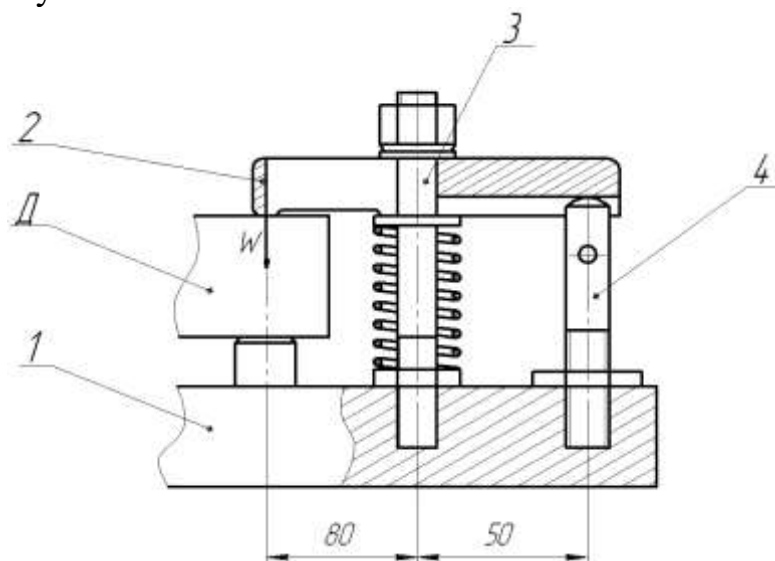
Схема прихвата: 1 – основание; 2 – прихват; 3 – шпилька; 4 – упор; Д- деталь
